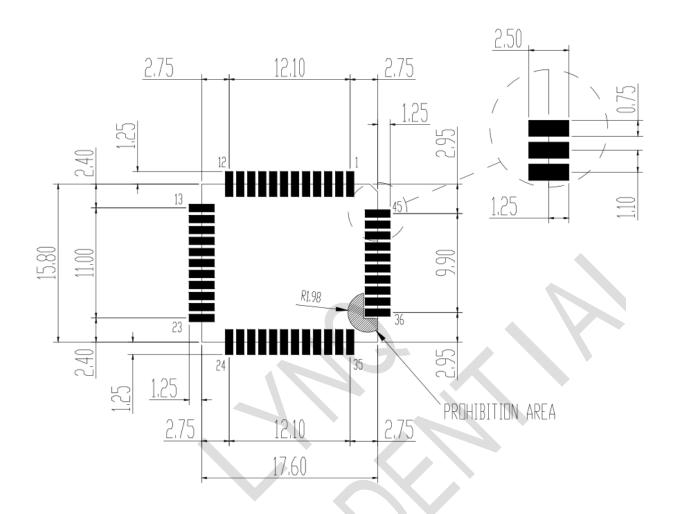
模块推荐焊盘 (Top view 单位: mm)
